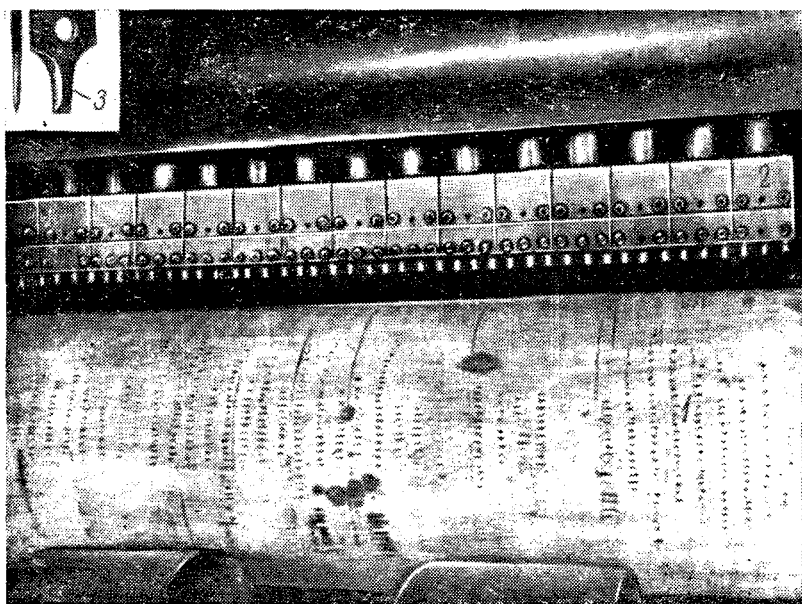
Наколочный станок для бревен и столбов, работающий по принципу долбяка (США):
